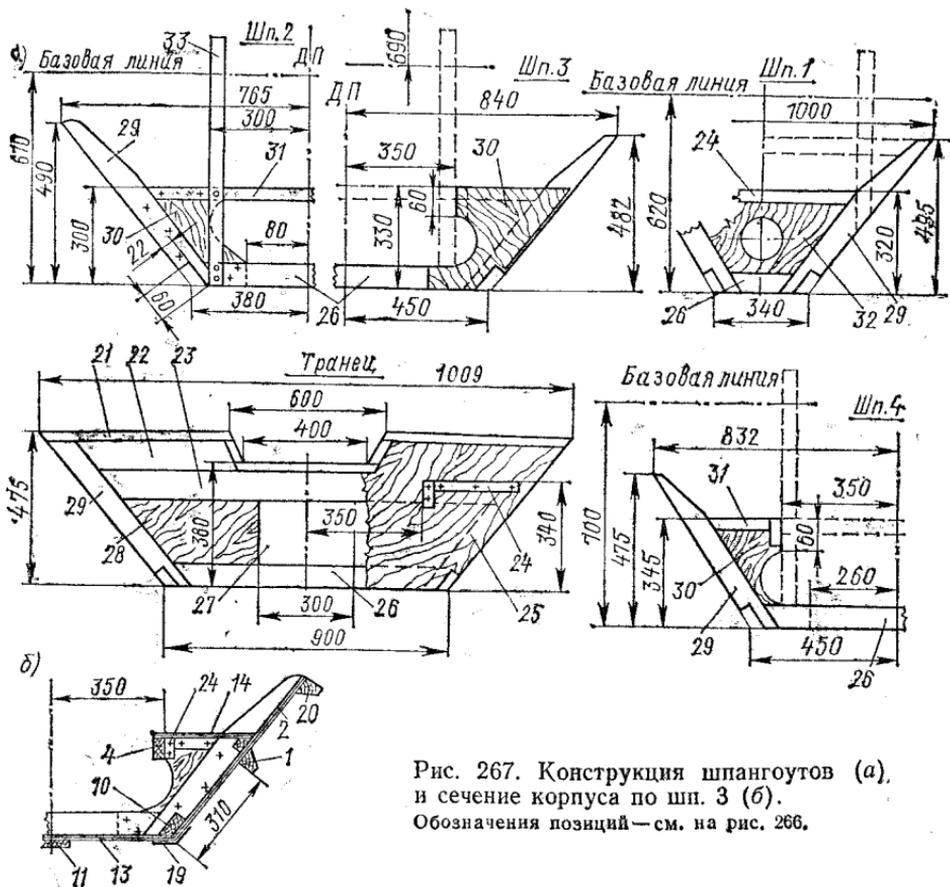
Конструкция шпангоутов (а), и сечение корпуса по шп. 3 (б).
